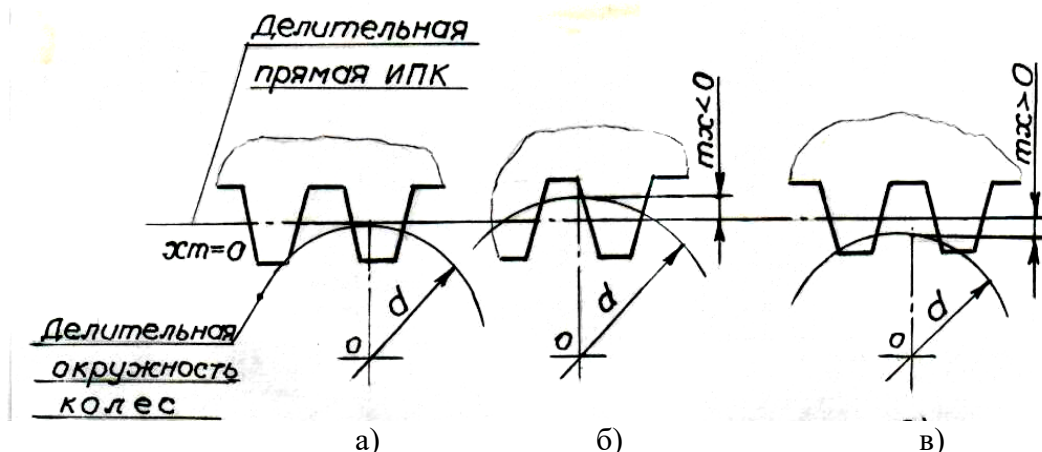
Установка инструмента относительно зубчатого колеса:
